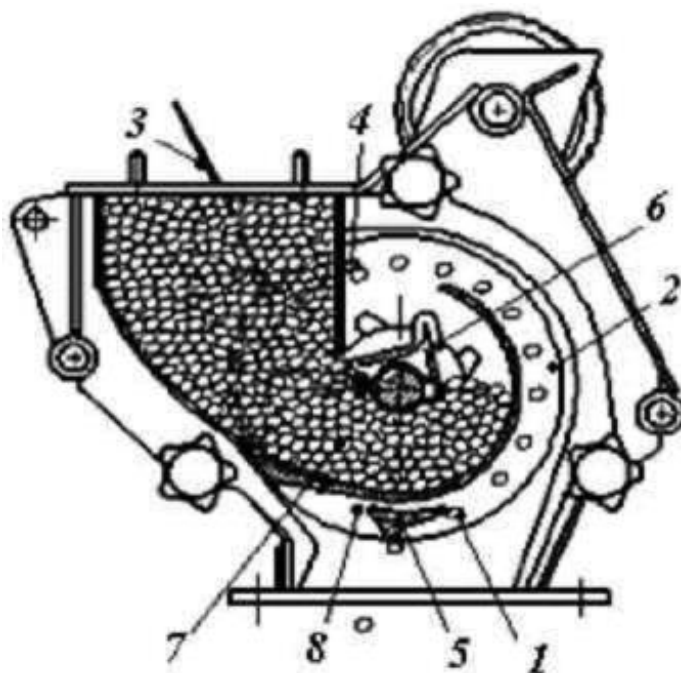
Схема высевающего аппарата: 1 – семена; 2 – высевающий диск; 3 – сводоразрушитель; 4 – отражатель «лишних» семян; 5 – сбрасыватель-направитель; 6 – ворошитель семян; 7 – семенная камера; 8 – присасывающее отверстие
